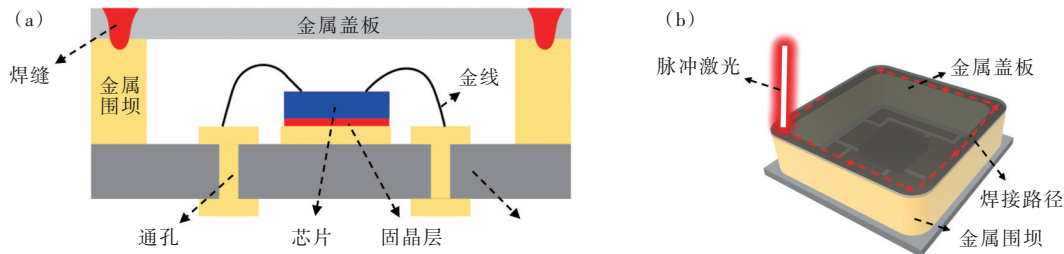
(a)三维 DPC 陶瓷基板激光封焊结构示意图;(b)三维 DPC 陶瓷基板激光封焊示意图
